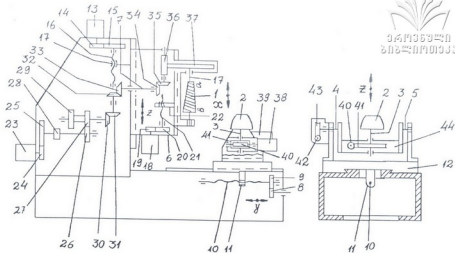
Кинематическая схема зубофрезерного станка с ЧПУ для нарезания эллипсоидных, сферических, торондных, некрутлых и круглых конических колес
